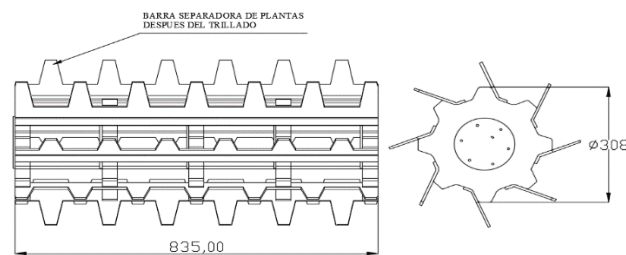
Dimensiones geométricas del cilindro separador de mieses
